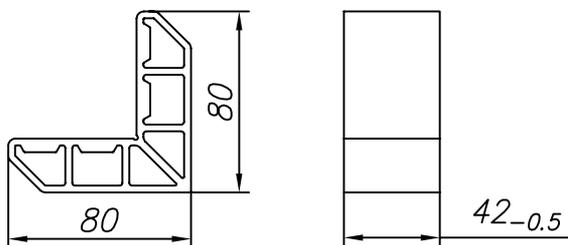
Изготовление соединителя углового FLGU.400.0914
